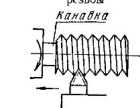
Канавка для выхода резьбового резца при нарезании наружной резьбы
